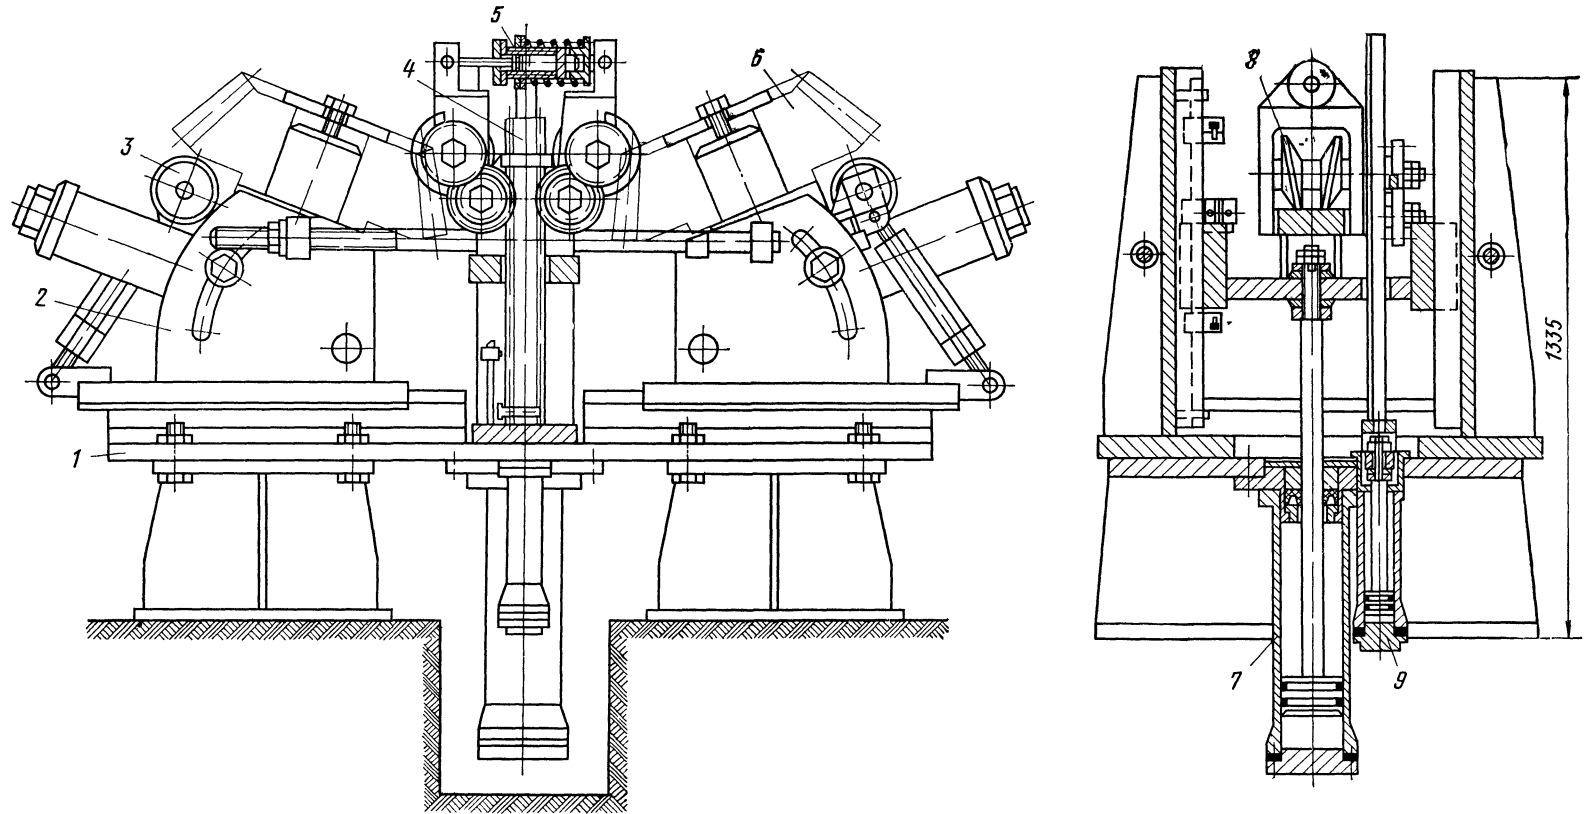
Полуавтоматический станок для обкатки конических зубчатых колес:
